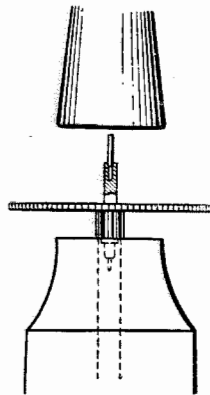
Положение сверла в приспособлении для сверления осей.
